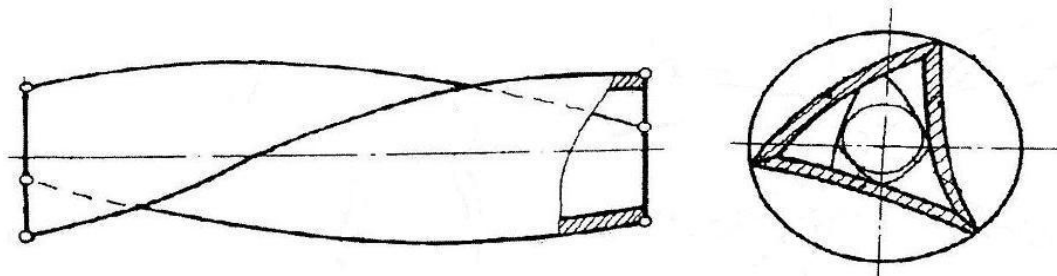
Релятивный цилиндрический винтовой барабан РЦ 7.1.a
